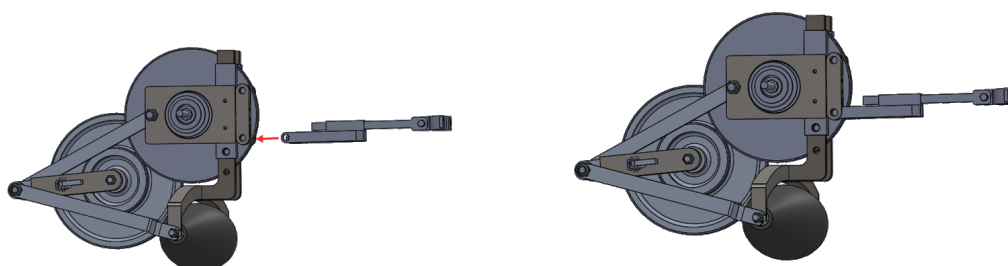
Assemblage de la glissière de fixation et du prototype
